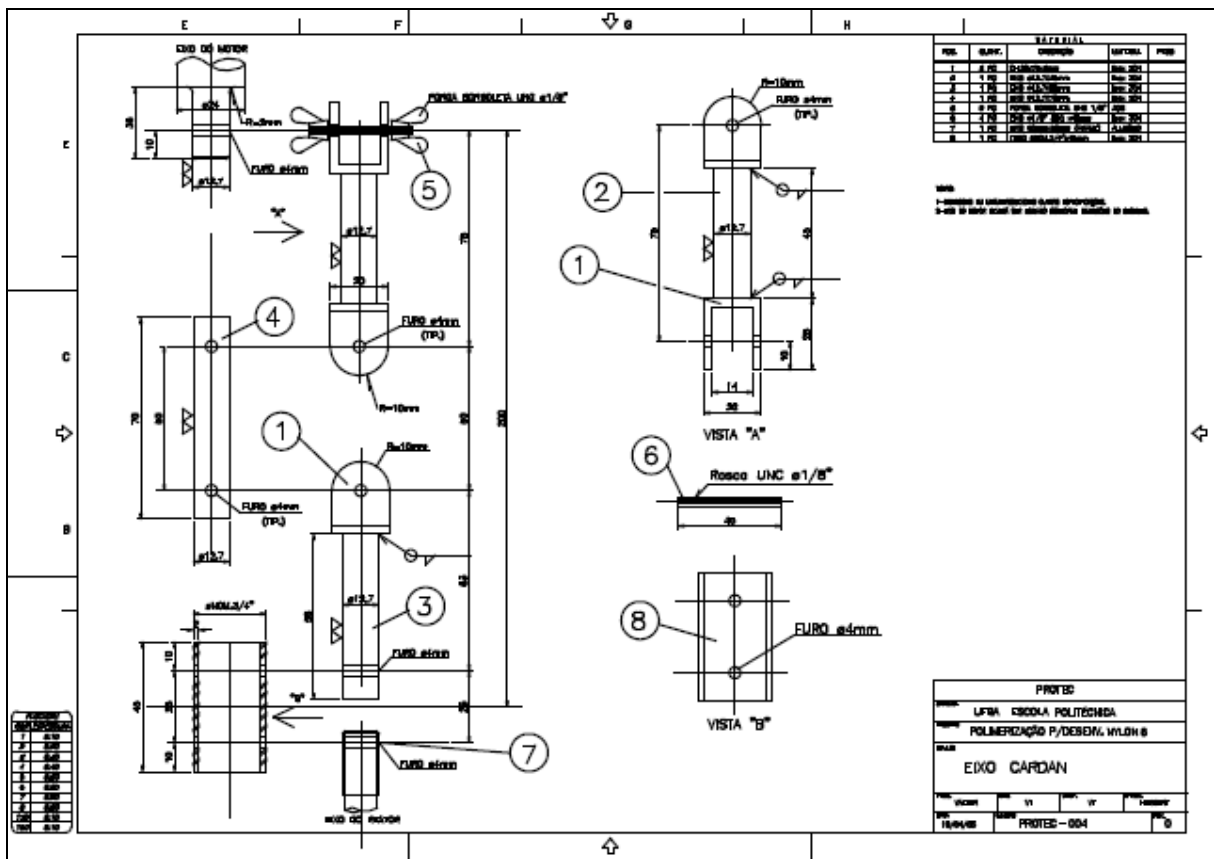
Desenho mecânico e construtivo do eixo Cardan.
